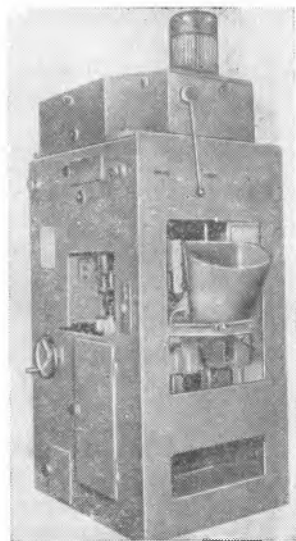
Роторный пресс ФПР-16 для формования кругов диаметром 60—80 мм
